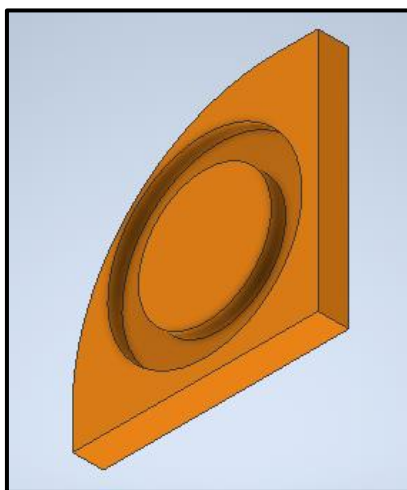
Diseño de la pieza de protección de la tornillería 1 del dispositivo.
